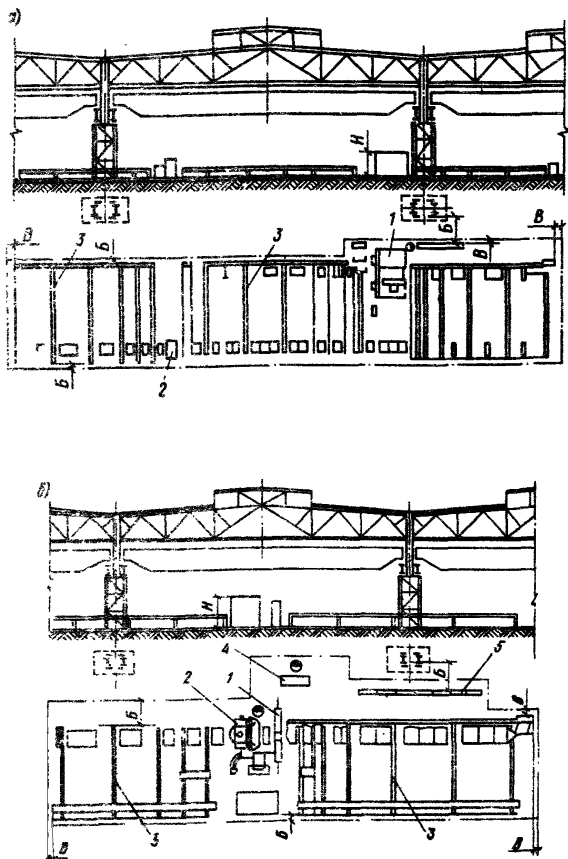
Размещение поточной линии для резки и сверления отверстий в швеллерах и балках фирмы "Вагнер" с агрегатным сверлильным станком (а), со сверлильным станком (б)
